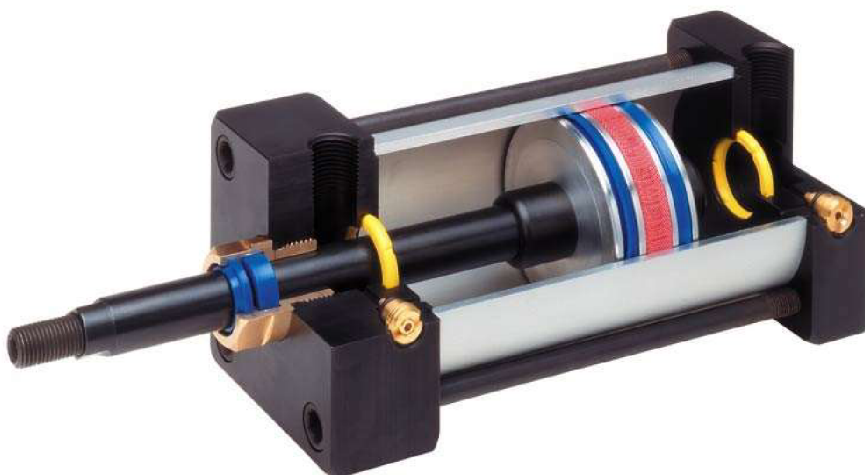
příklad pneumaticko-hydraulického multiplikátoru [11]
